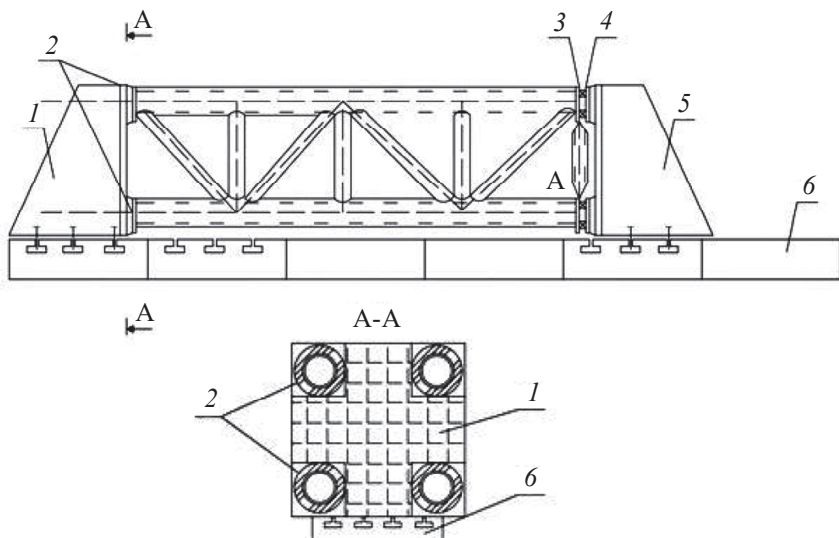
Установка для укрупнительной сборки секций мачт:
